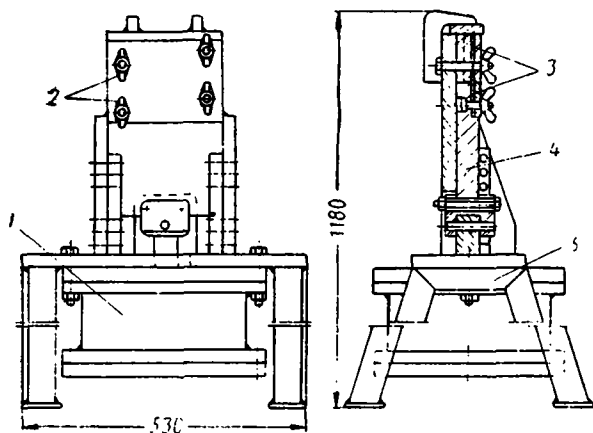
Приспособление для формовки перехода из слоя в слой при намотке двухслойных катушек
